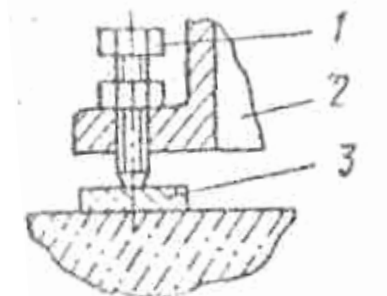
Установка оборудования на подкладке и винтовой опоре:
